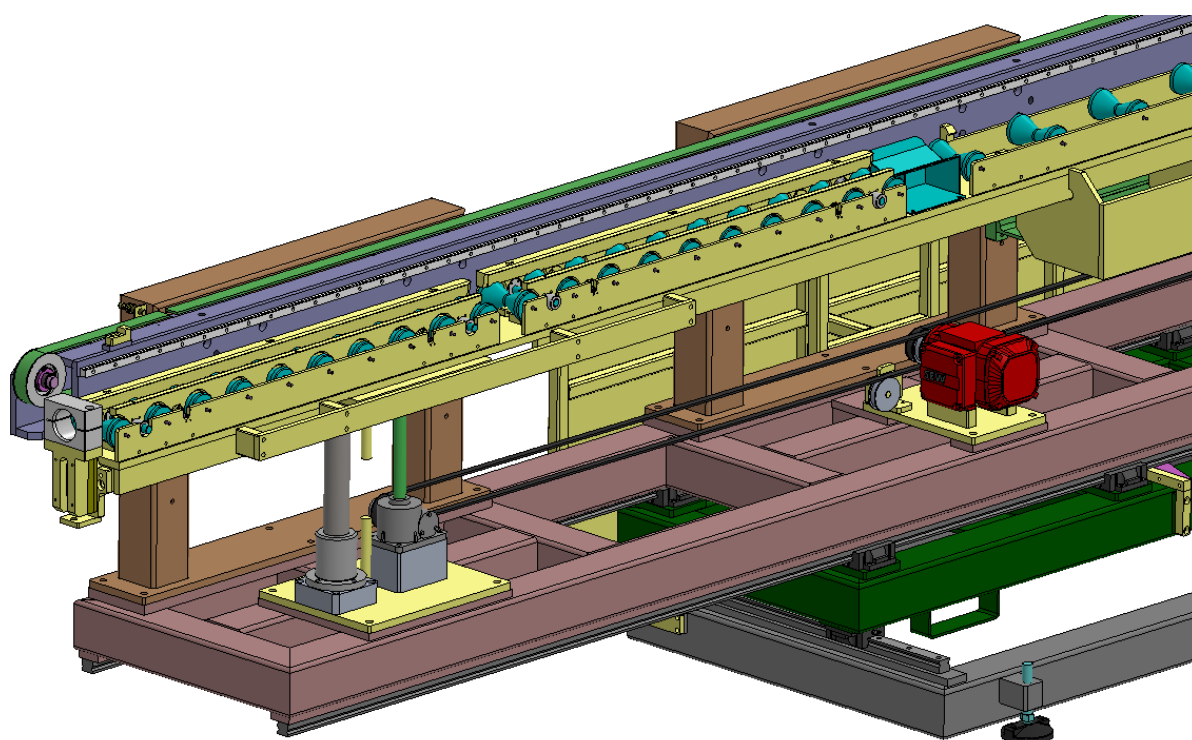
Tlačné řetězy – spodní pracovní poloha
